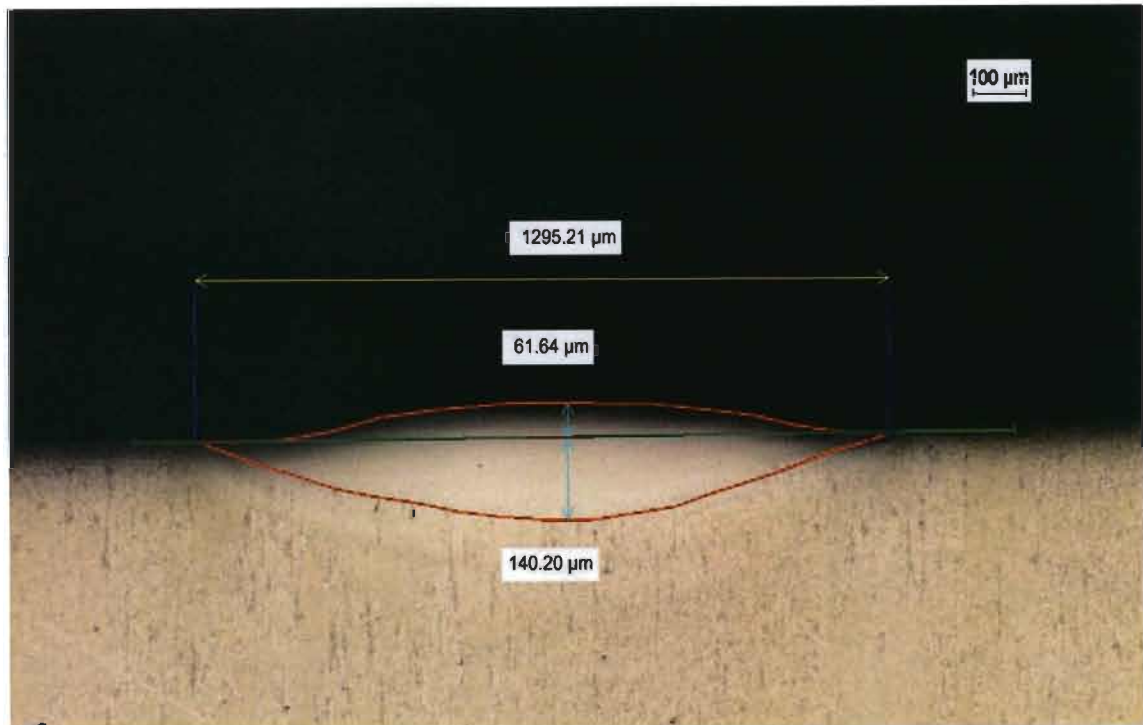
8 Cordón de soldadura 4 visto a 5X
